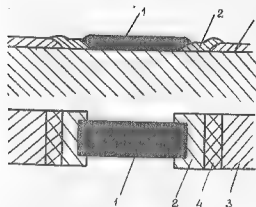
Резистор с выводом, реализованным внахлест: 1 — резистивный элемент; 2 — промежуточный металл; 3 — проводник из благородного металла; 4 — накладка
